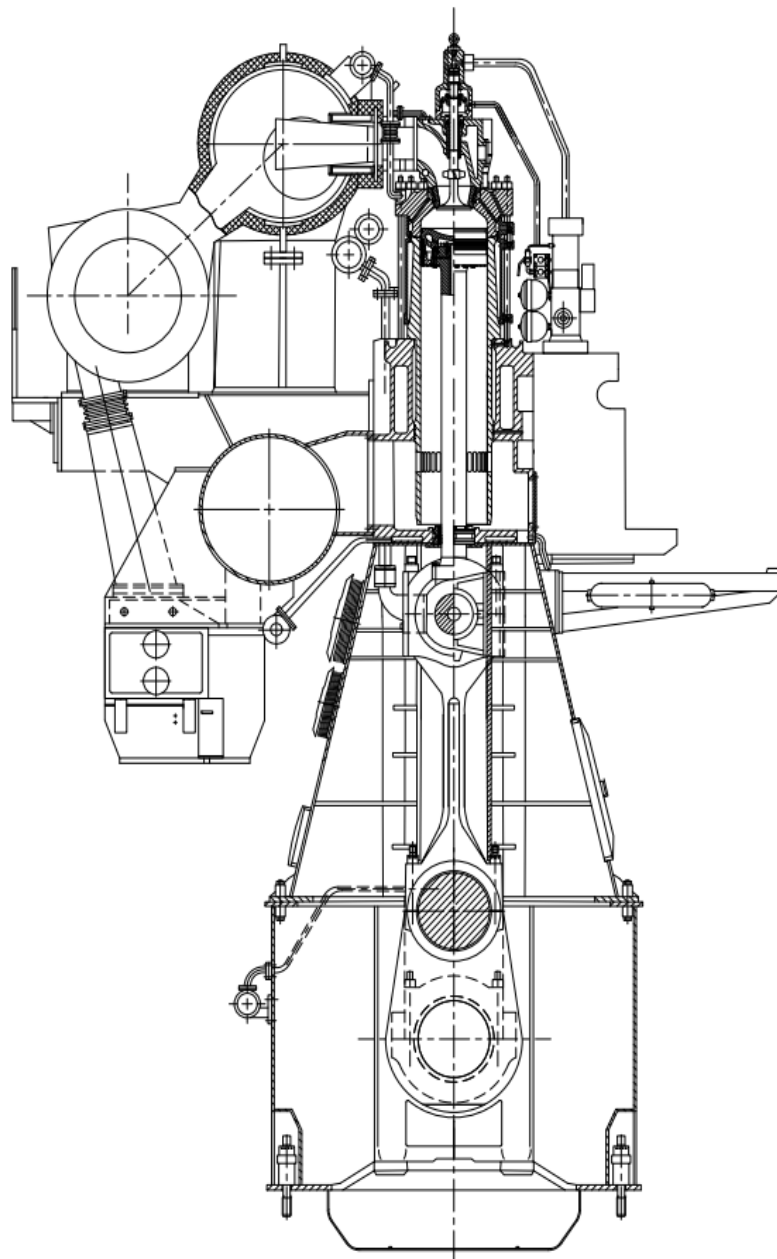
Поперечний переріз двигуна 6ДКРН 50/221,4
